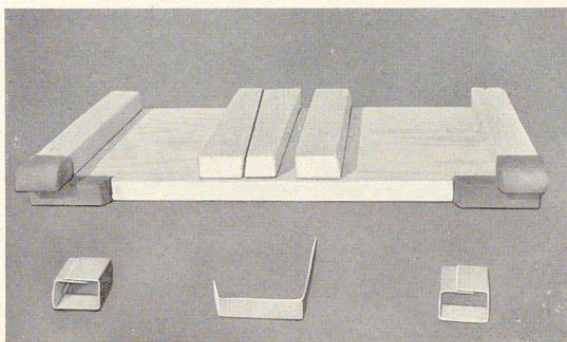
Das Schlittenbrett mit Lufer und Keilvorrichtung und den Unterlagsblechen fur Lufer und Schlittenbrett
